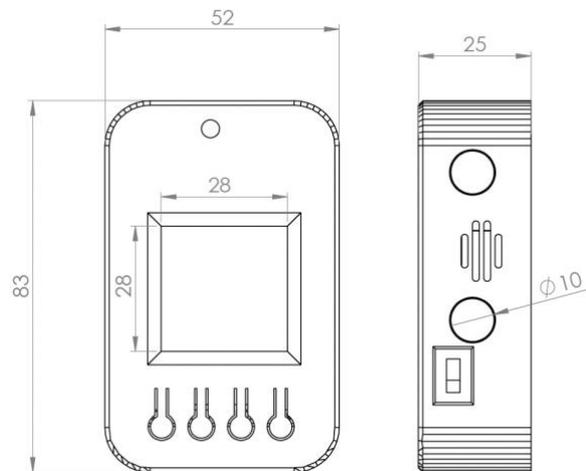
Dimensões sensor portátil (Fonte: o autor)
